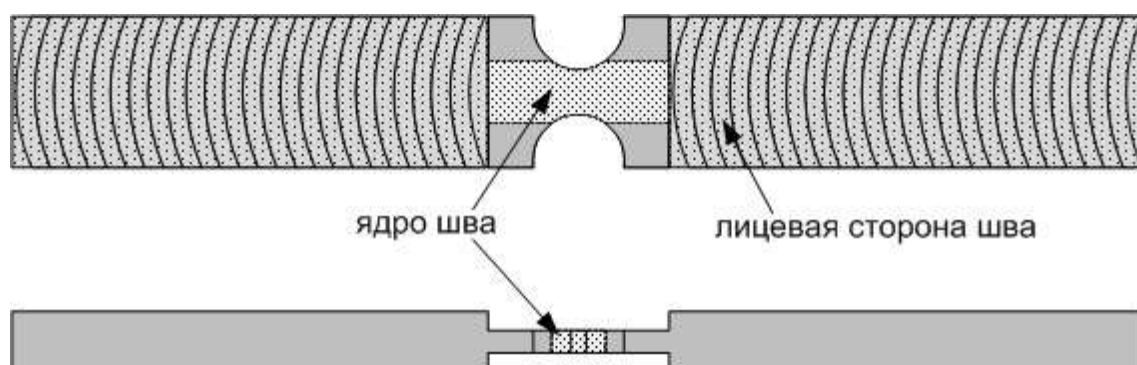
Схема вырезки образцов для испытаний из зоны перемешивания сварного соединения
